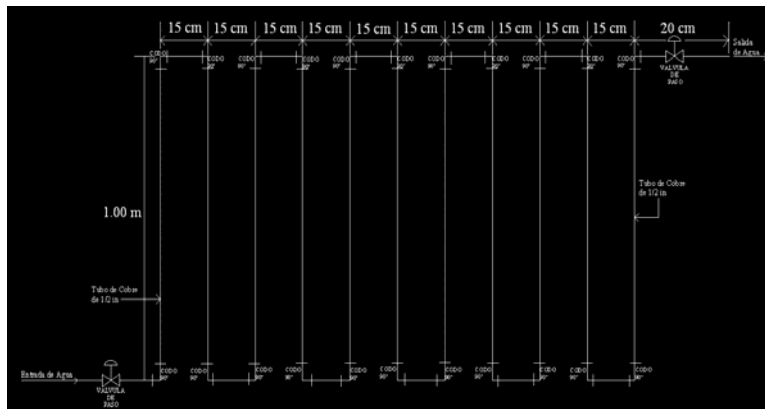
DIMENSIONES DEL CALENTADOR SOLA PLANO.
